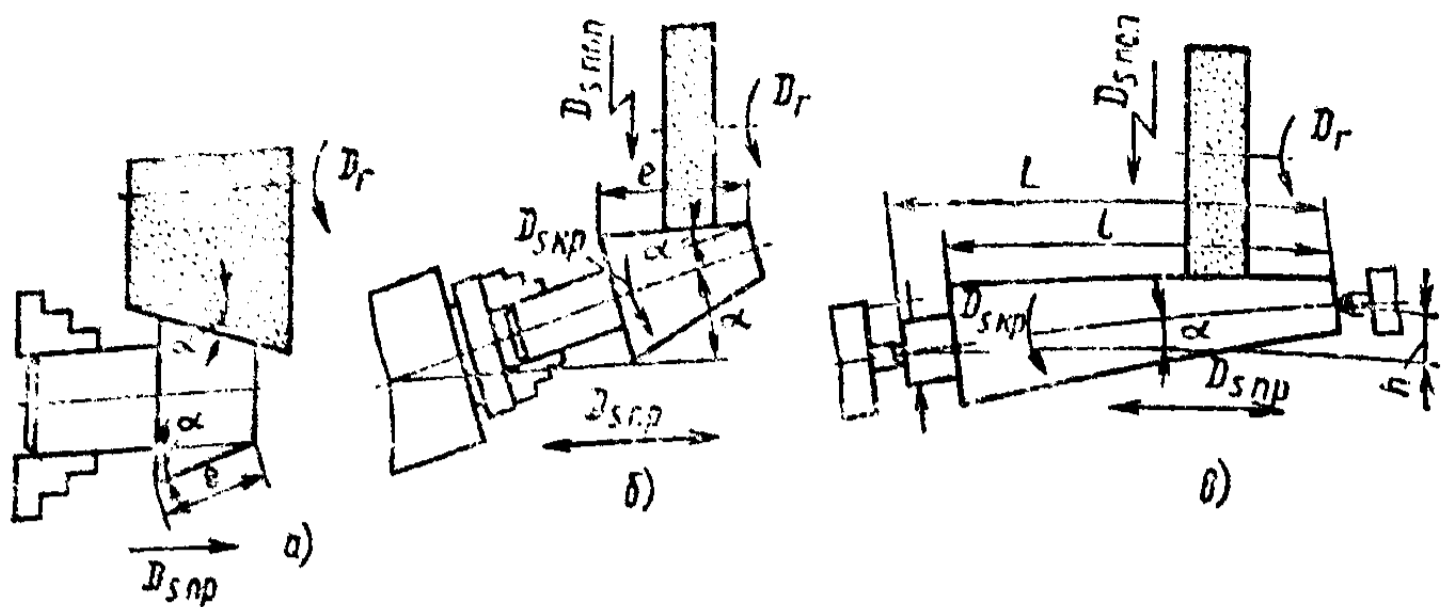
Схемы обработки конических поверхностей на круглошлифовальном станке
